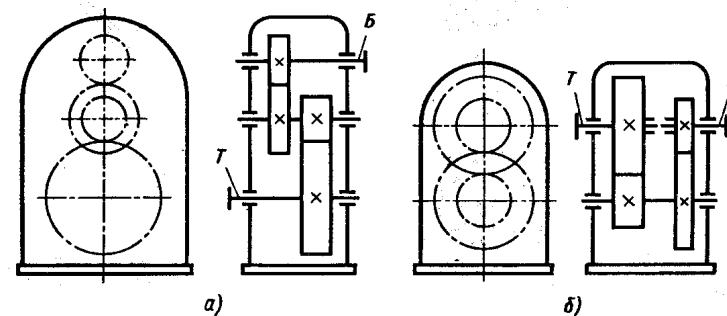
Кинематические схемы двухступенчатых цилиндрических вертикальных редукторов: а – выполненного по развернутой схеме (трехосного); б – соосного
